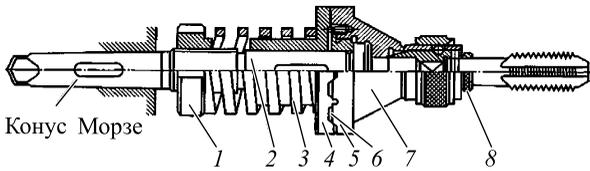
Предохранительный патрон для нарезания резьбы в глухих сквозных отверстиях:
